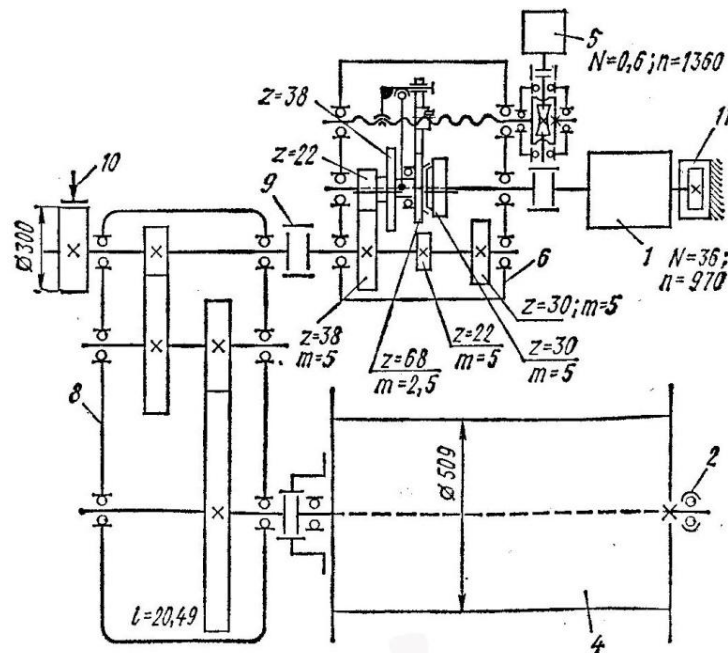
Кинематическая схема лебедки с дополнительным редуктором
